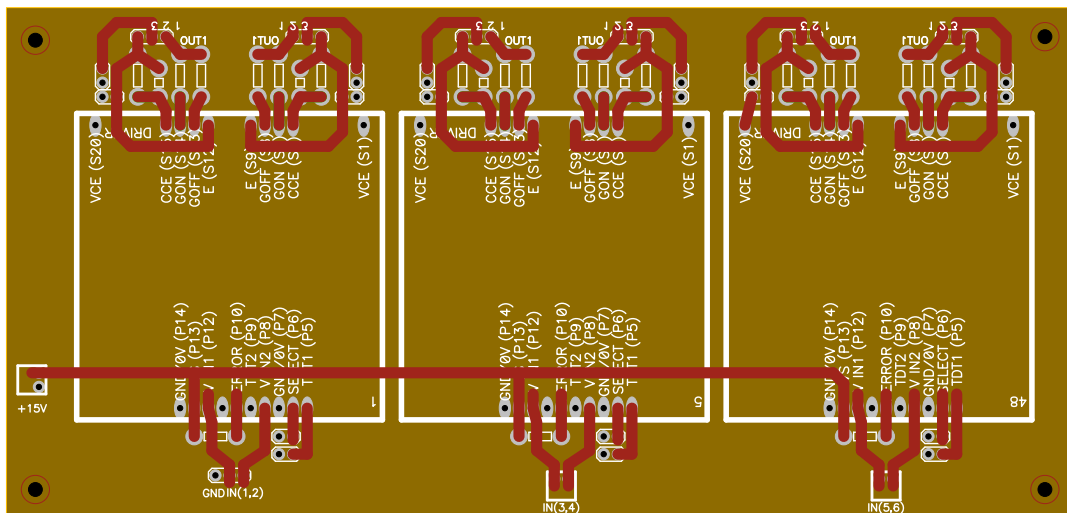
Desenho da placa de circuito impresso para os drivers SKHI22BR
